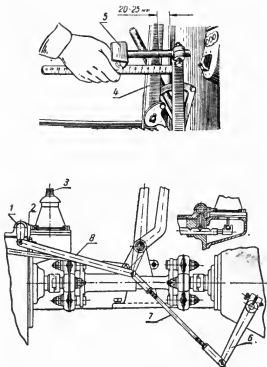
Регулировка механизма блокировки и управления центральной муфтой сцепления тракторов ДТ-54 и ДТ-54А:
